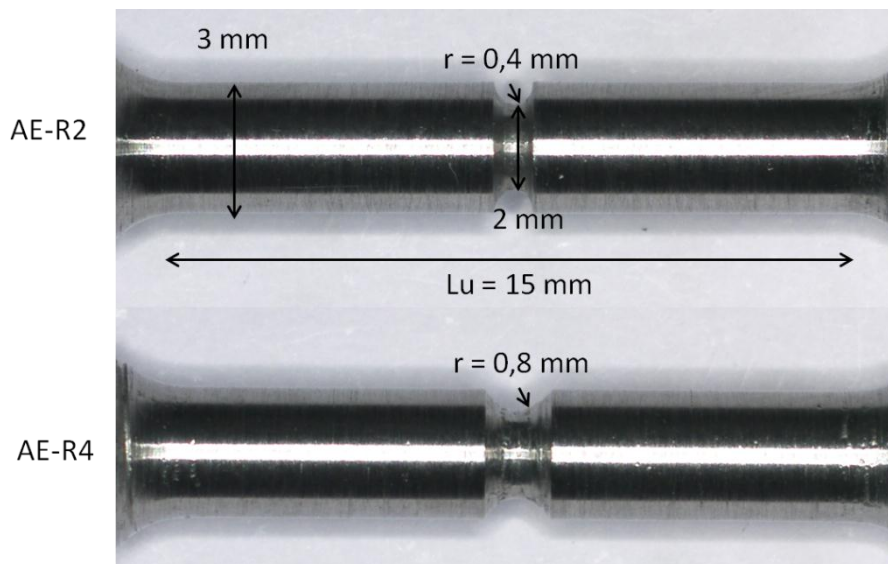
Dimensions des éprouvettes de type axisymétrique entaillée de type AE-R2 et AE-R4, dont le rayon d'entaille est respectivement de 0,4 mm et 0,8 mm.
